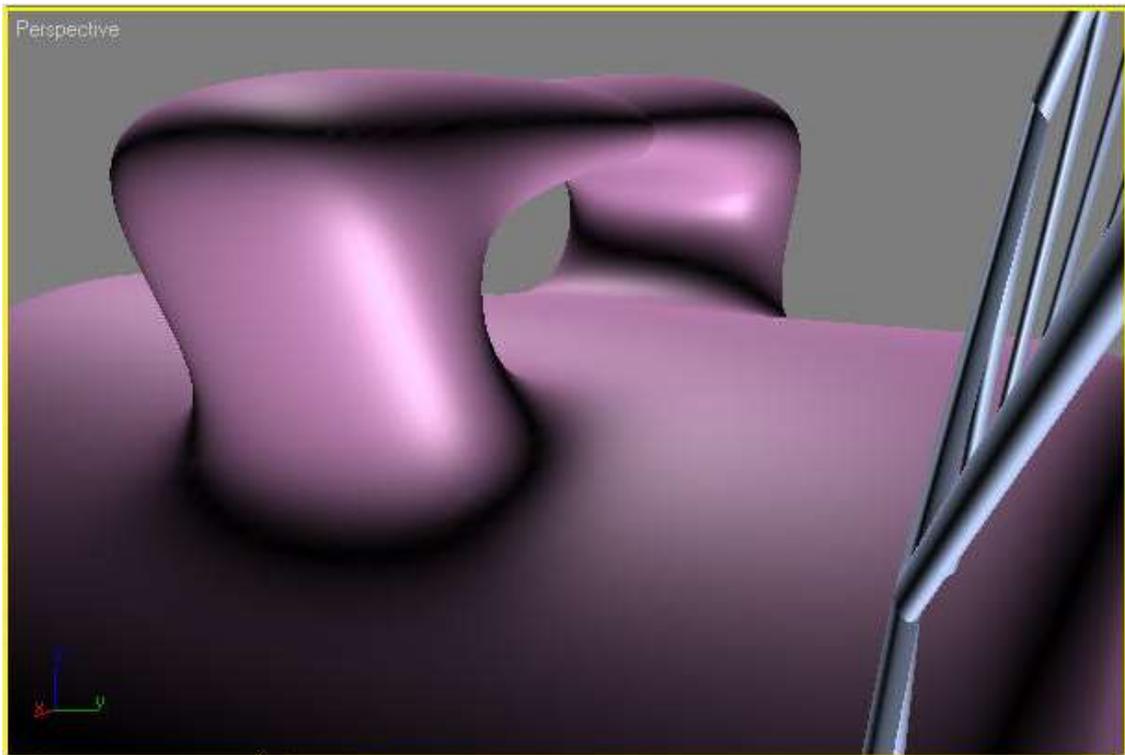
Ручка на корпусе мотора для удобного переноса вентилятора
